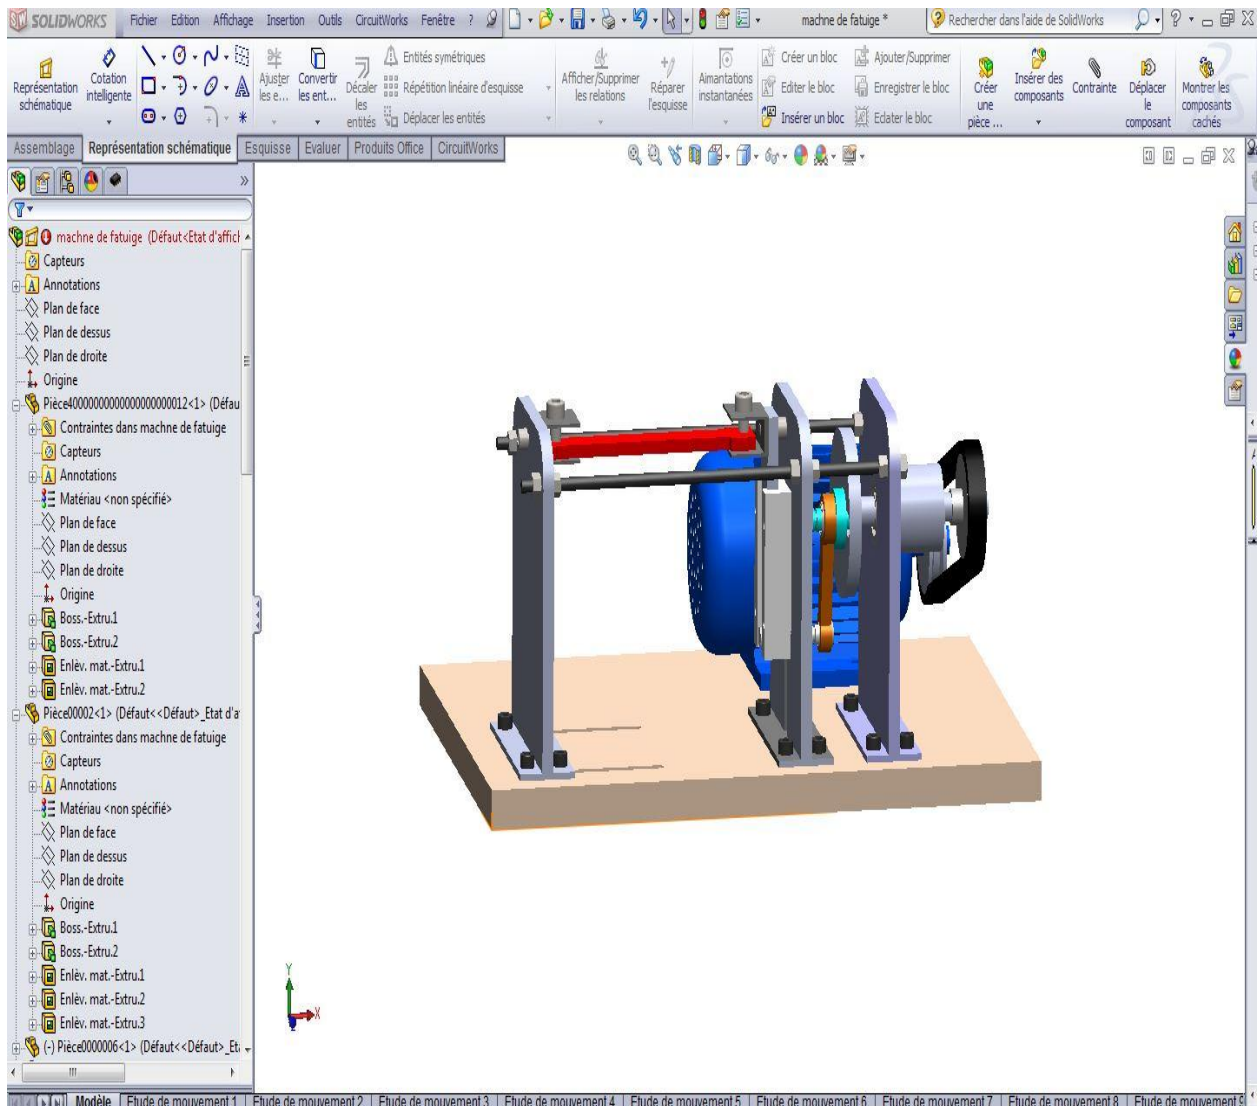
Vue de machine réalisée sous SOLIDWORKS
